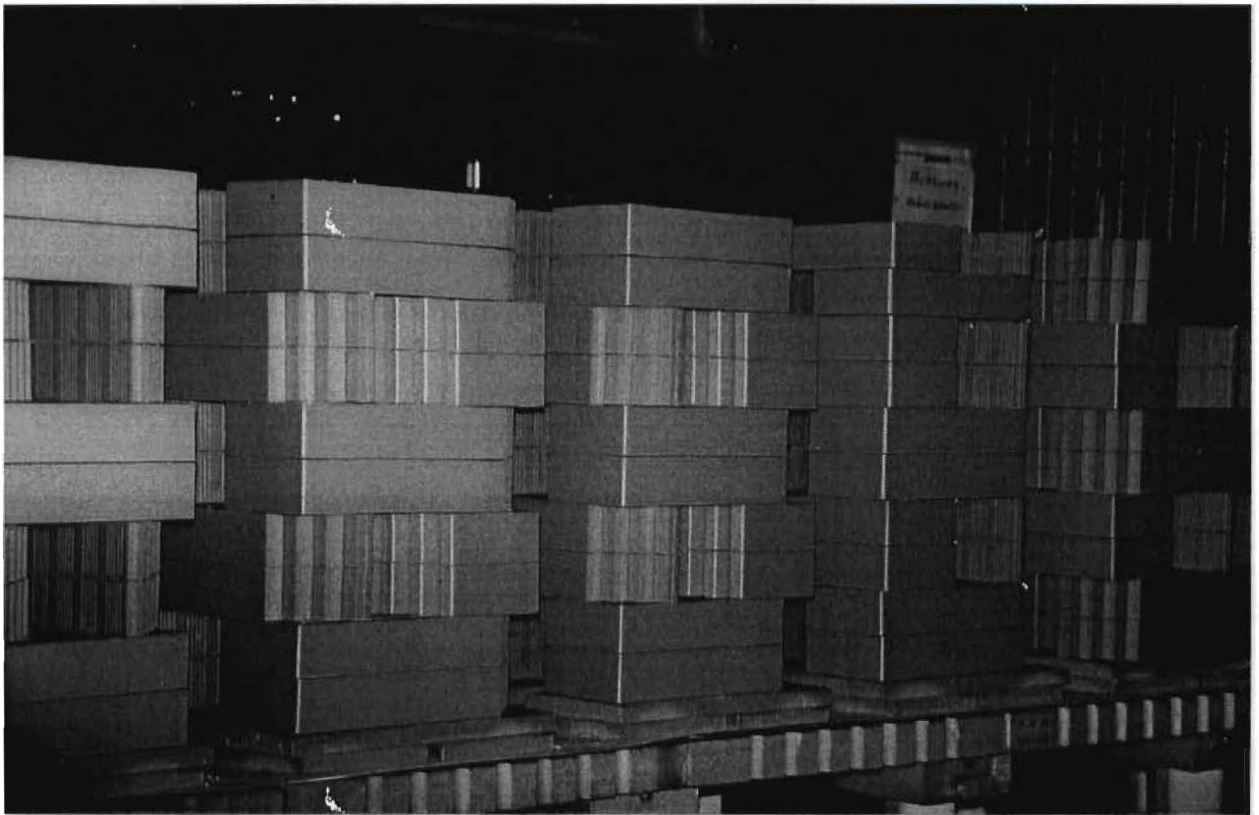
Voll bestückter Ofenwagen; die Schwindplatten sind deutlich zu sehen.
